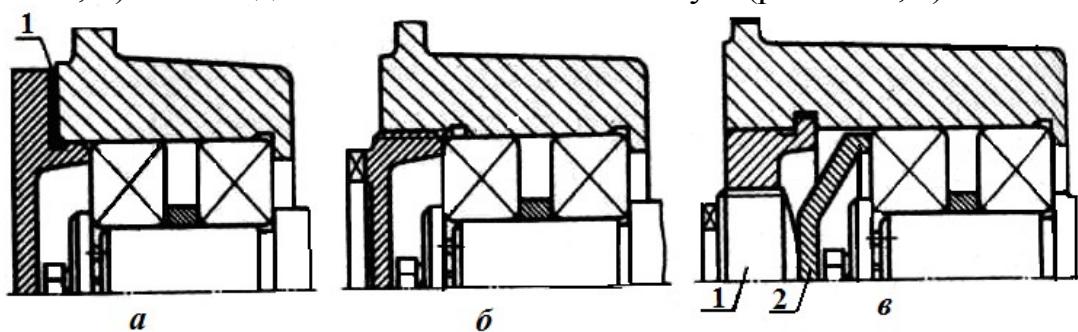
Способы осевого смещения наружных колец подшипников
